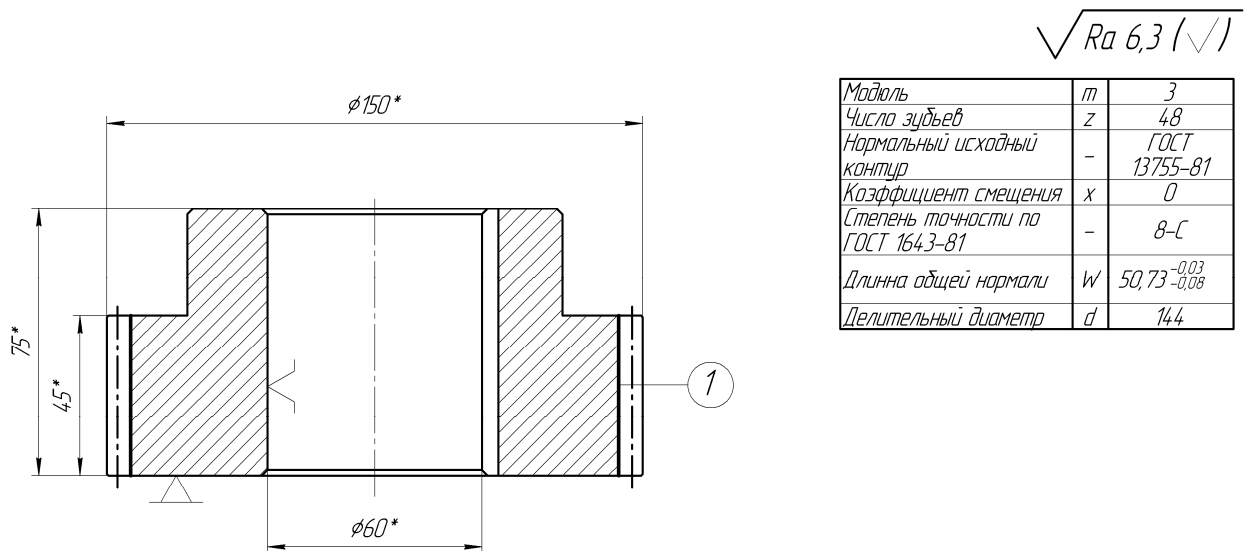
Операционный эскиз зубофрезерной обработки
